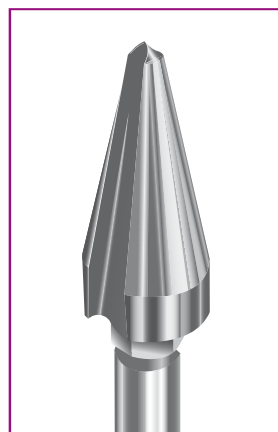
Kegelbohrer für Wellplatten PLEXIGLAS® WP
